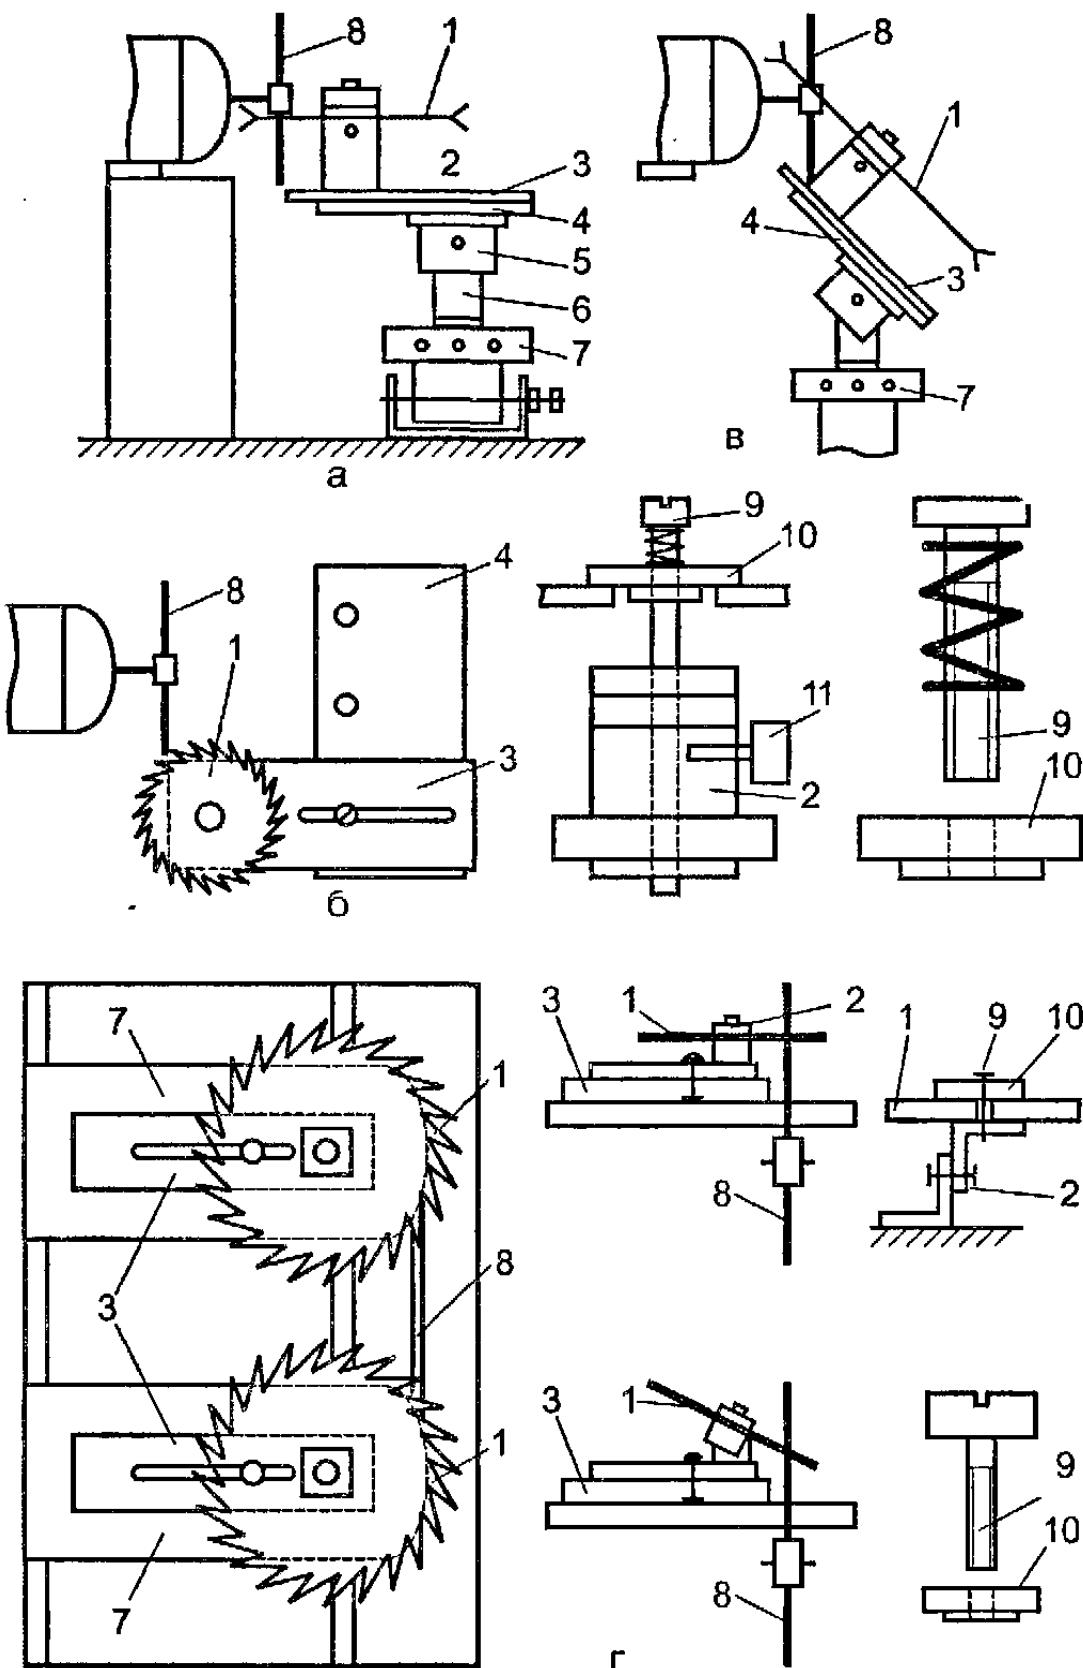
Механизмы для заточки круглых пил и насадных фрез:
